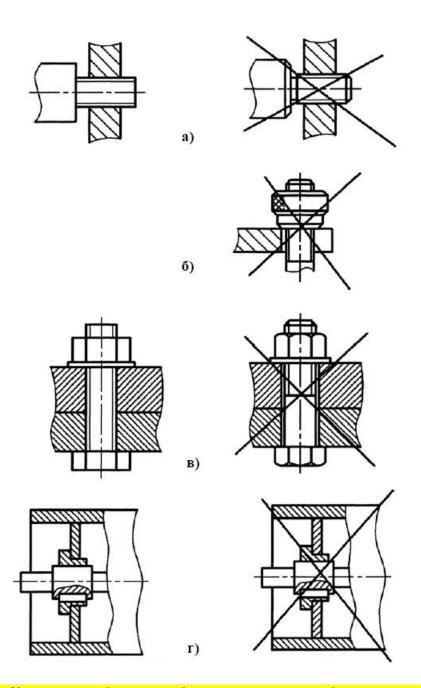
Упрощенные изображения на сборочных чертежах: а - резьбовое соединение; б - гайка с накаткой; в - болтовое соединение; г - сварная деталь
